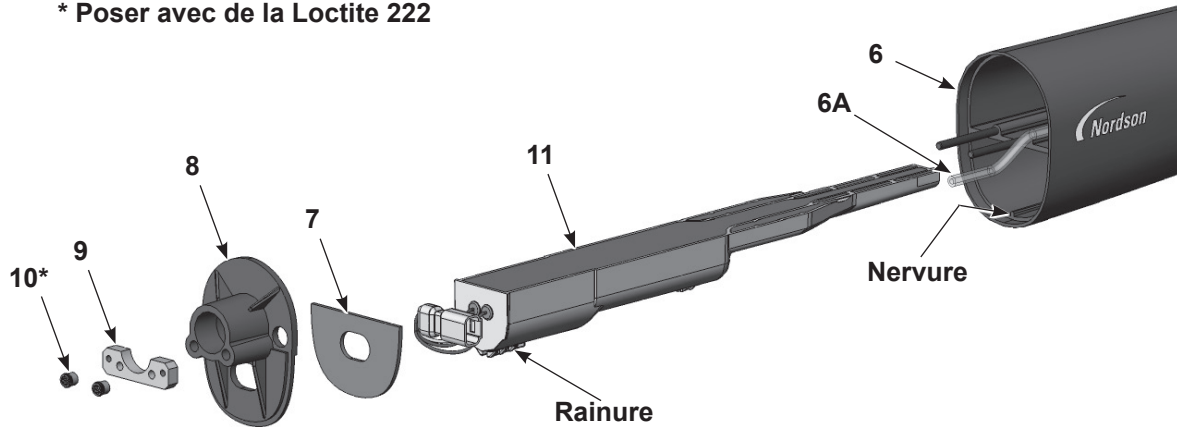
Démontage du pistolet à fixation sur barre 2 sur 3
